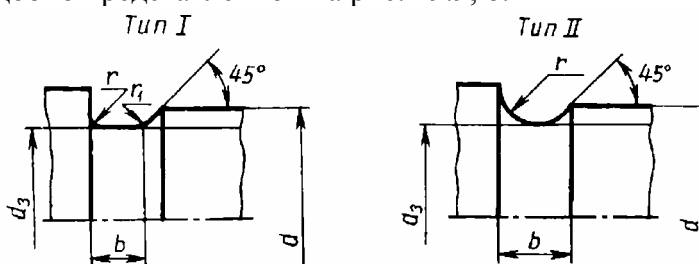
Канавки для выхода резьбонарезного инструмента
